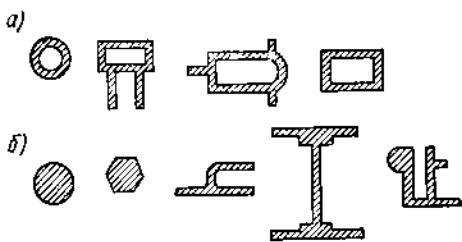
Примеры профилей, получаемых прессованием: а — полые; б — сплошные
